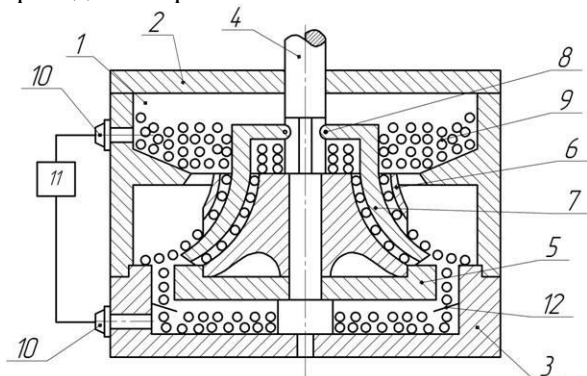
Схема вибрационной обработки каналов, 1 – контейнер; 2 – крышка контейнера; 3 – емкость для рабочей среды; 4 – вал привода; 5 – базовая опора для заготовки 6; 7 – твердосплавные вставки, установленные на поворотном узле 8; 9 – жидкая рабочая среда с твердым наполнителем; 10 – штуцеры для подачи и удаления рабочей среды, поступающей от насоса 11; 12 – расходомеры для регулирования в контейнере рабочей среды
